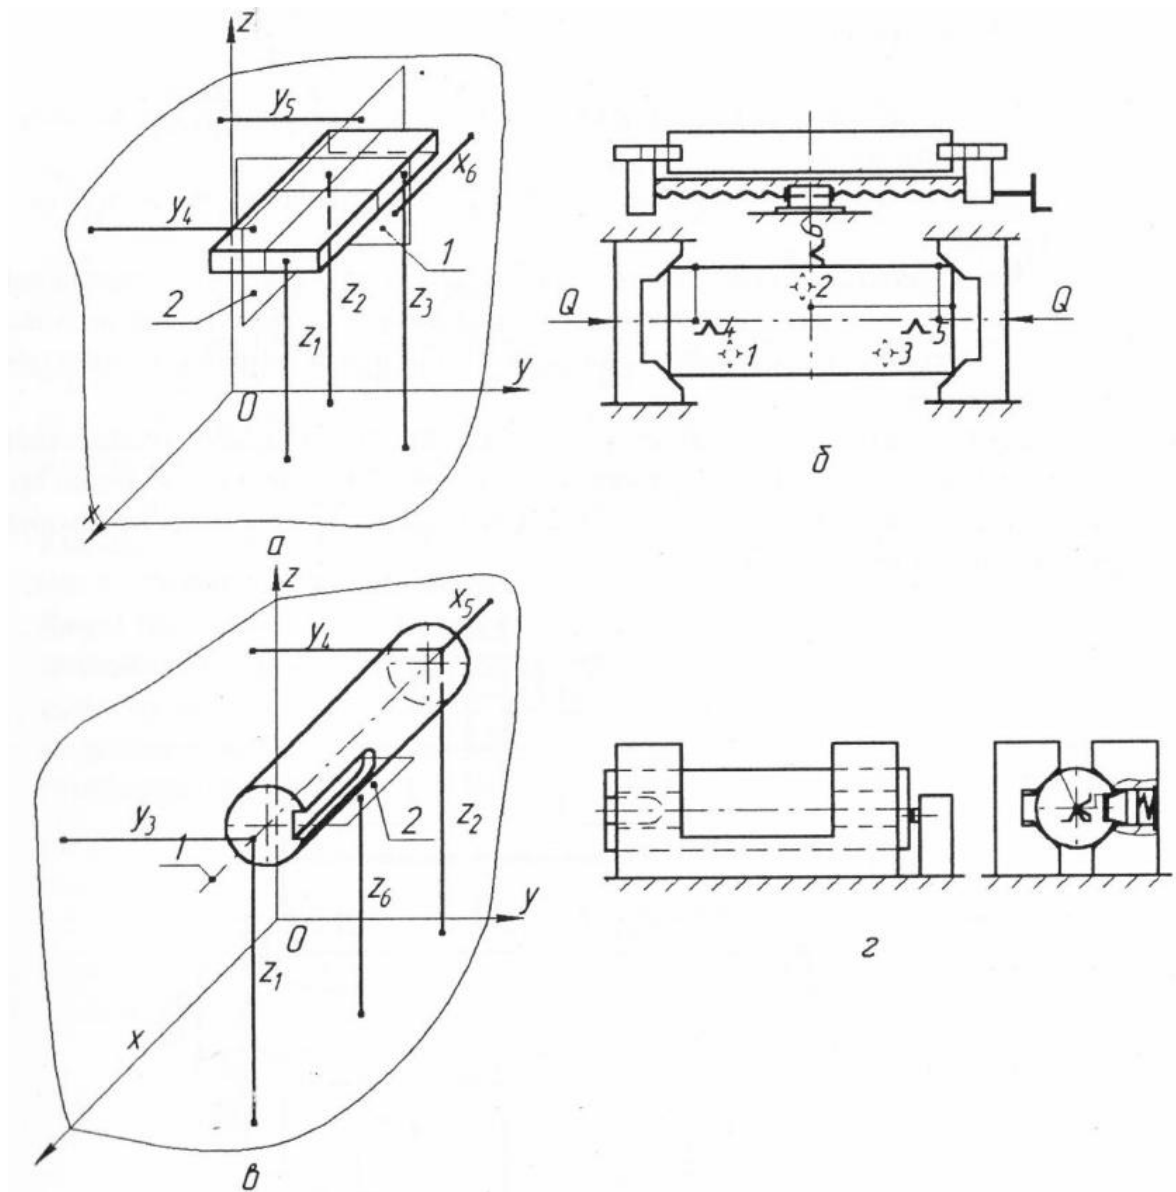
Схеми базування: а) призматичного тіла; б) реалізація схеми базування призматичного тіла; в) циліндра; г) реалізація схеми базування циліндра
